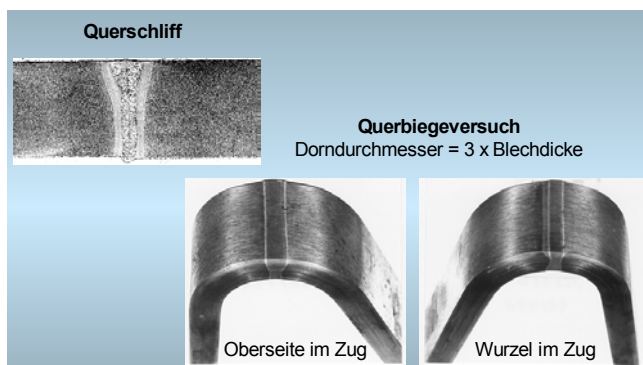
Fallproben einer XABO 960-Schweißverbindung, Blechdicke 10 mm
